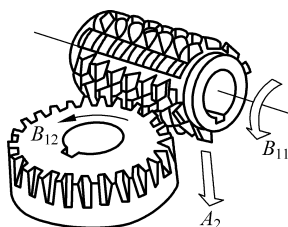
用齿轮滚刀滚切直齿圆柱齿轮
